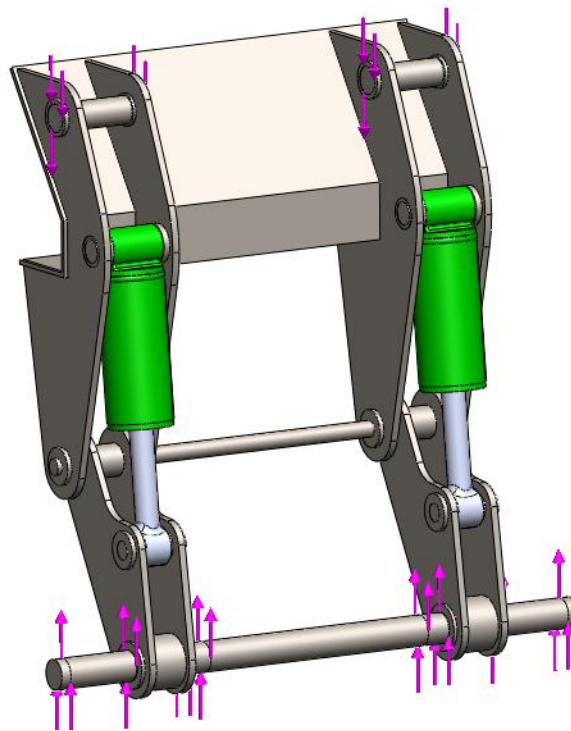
Cargas aplicadas al pie de apoyo.
